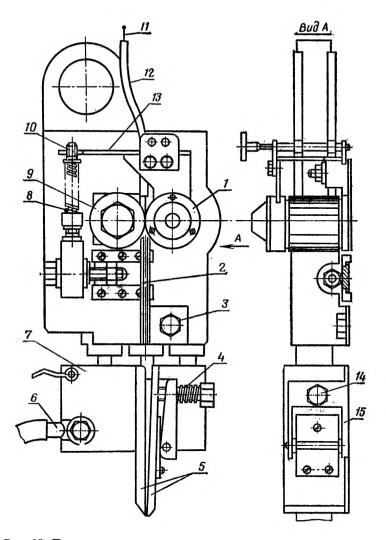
Приставка для наплавки стальным ленточным электродом:
